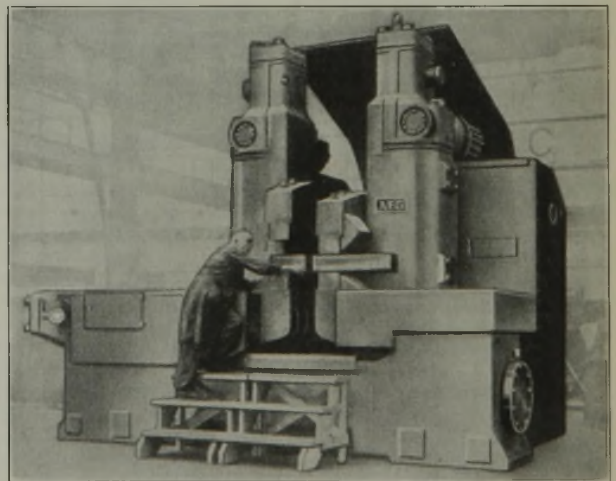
Selbsttätige Groß-Abschmelz-Stumpfschweißmaschine.
